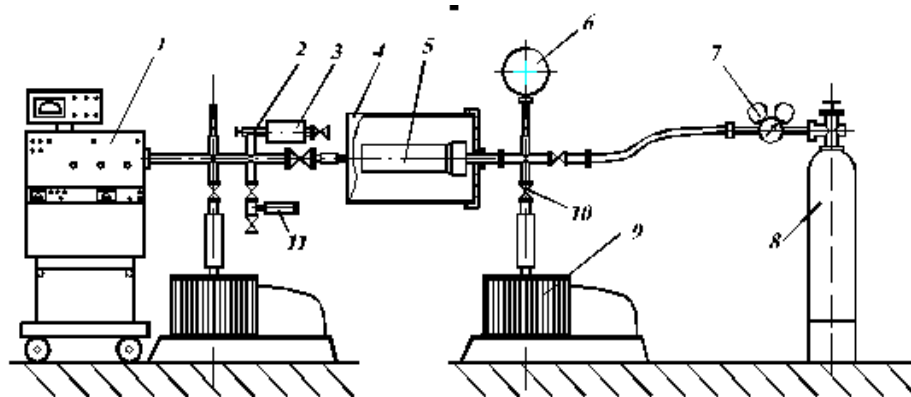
Схема установки для контроля герметичности способом вакуумной камеры: 1- гелиевый течеискатель; 2- натекатель; 3- баллон с аргоном; 4- камера; 5- изделие; 6- мановакуумметр; 7- редуктор; 8- баллон с гелием; 9- вакуумный насос; 11 – калиброванная течь
